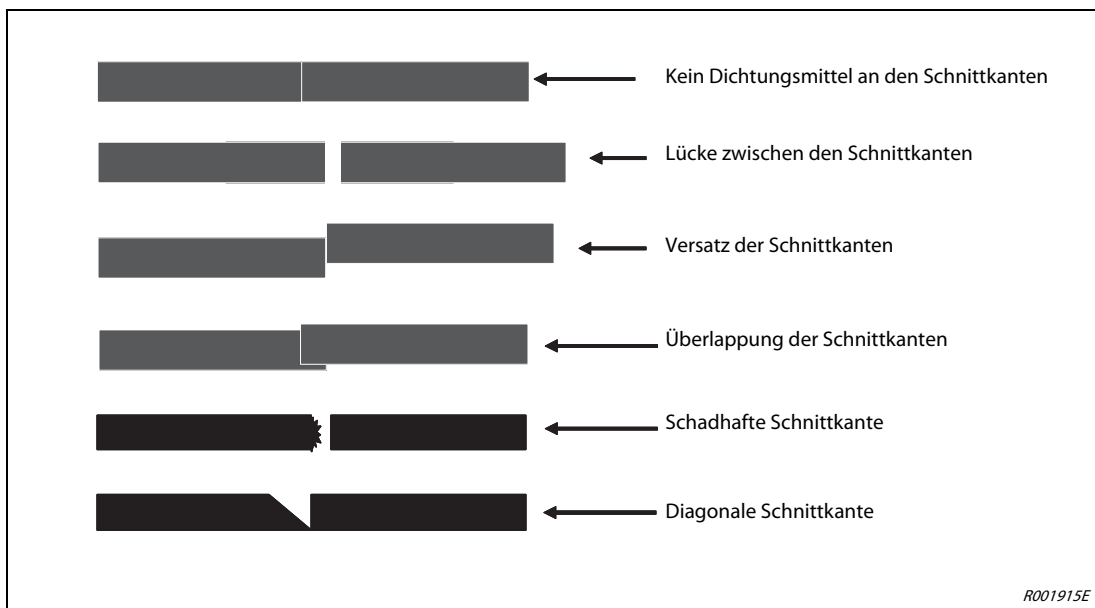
Dichtungsmittel auf die Schnittkanten geben
